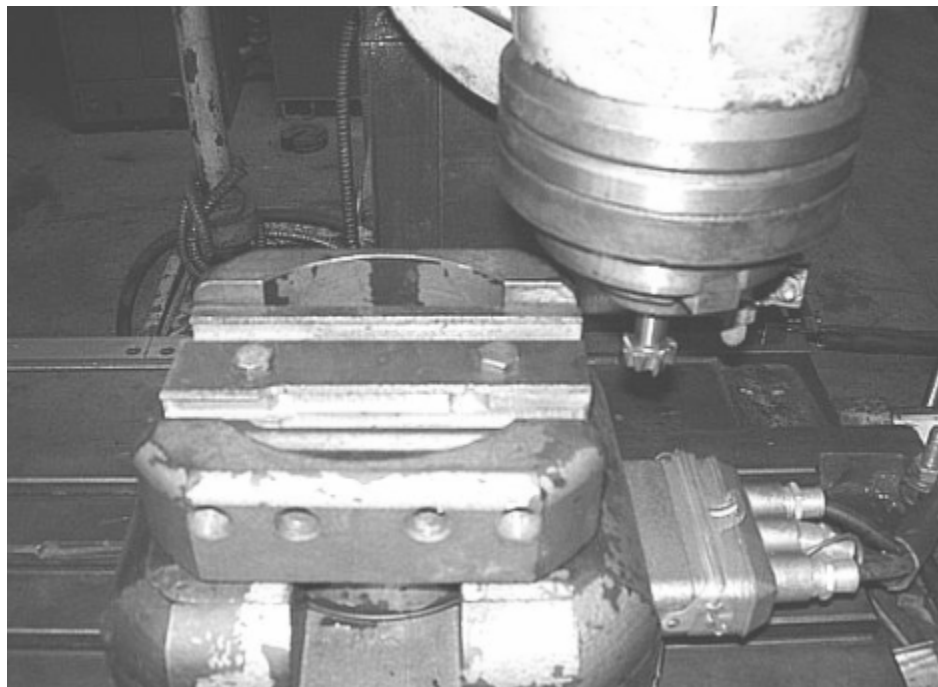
Внешний вид УДМ 600 с закрепленным столиком и заготовкой
